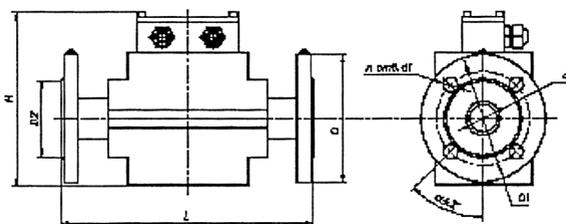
Габаритные и установочные размеры ПРПЭ типа ПРЭ.02
